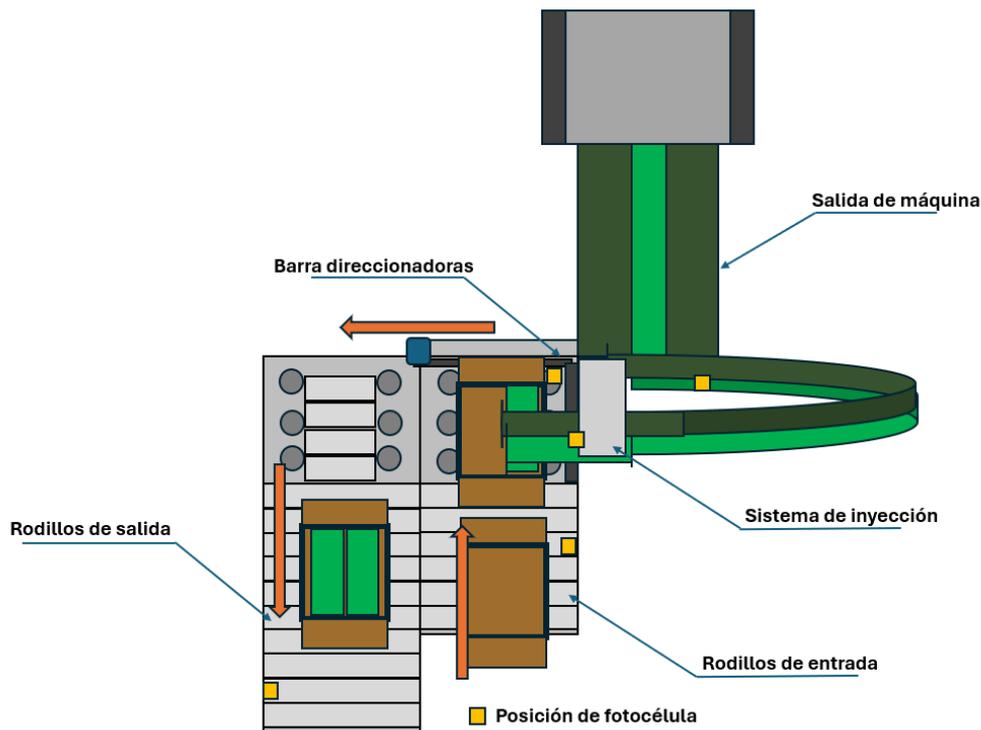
Solución planteada para la automatización de la salida de máquina (vista en planta)
